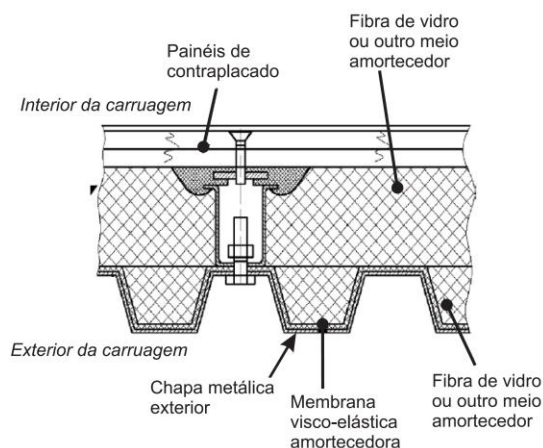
Secção transversal de um pavimento tipo de uma carruagem de passageiros com caixa construída em chapa de aço. Fonte: Fan e outros 2008, adaptado.
